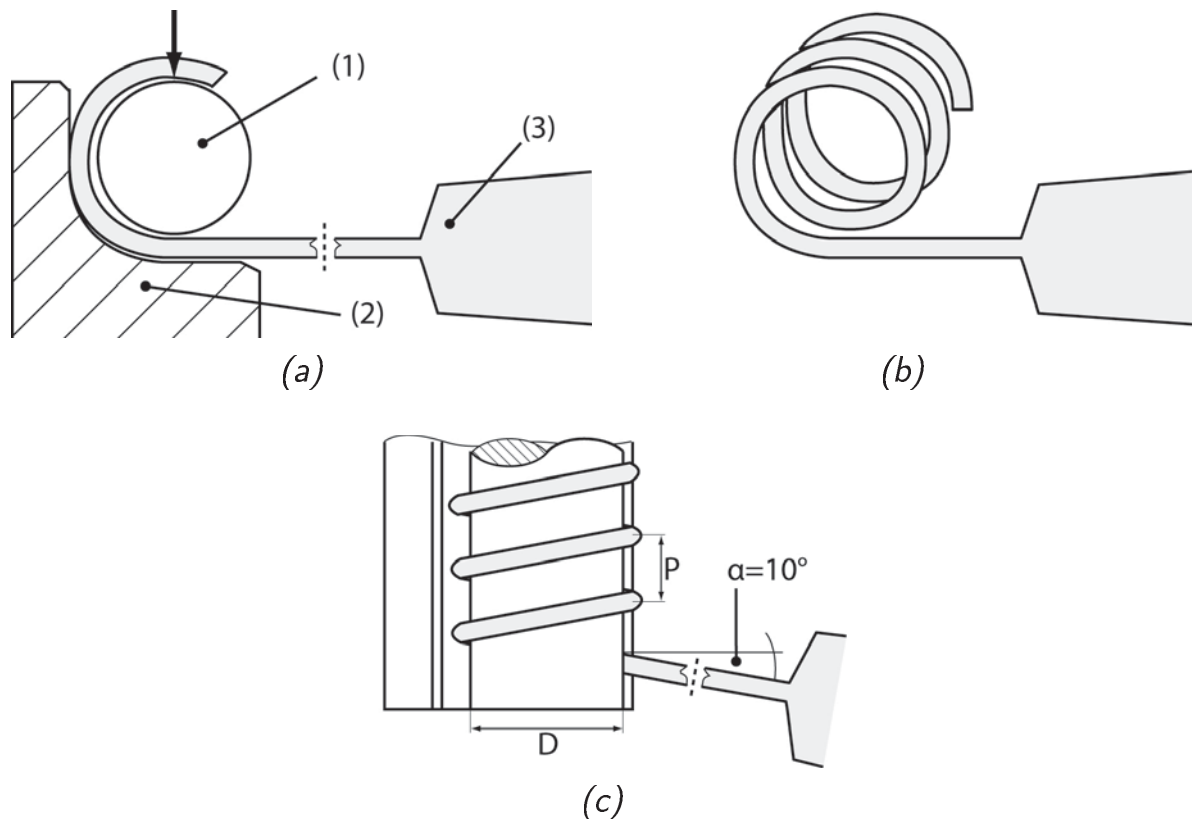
Rollbiegen einer Spule. Das stabförmige Halbzeug (3) wird zwischen Rollbiegewerkzeug (2) und zylindrischem rückfederndem Umformwerkzeug (1) geführt (Bild (a)) und zu einer Spule umgeformt (Bild (b)). Wird das Halbzeug unter einem Winkel α in das Rollbiegewerkzeug eingeführt, kann die Steigung der Wicklung eingestellt werden, Bild (c) in der Aufsicht.
